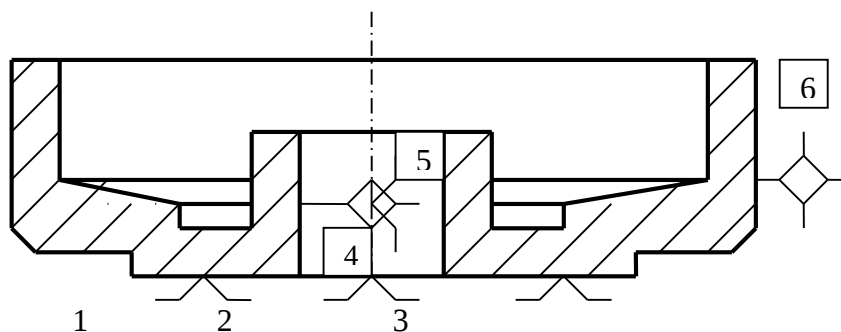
Теоретична схема базування деталі барабан: 1, 2, 3 - установчі бази; 4, 5 - подвійна опорна напрямна база; 6 - опорна.
